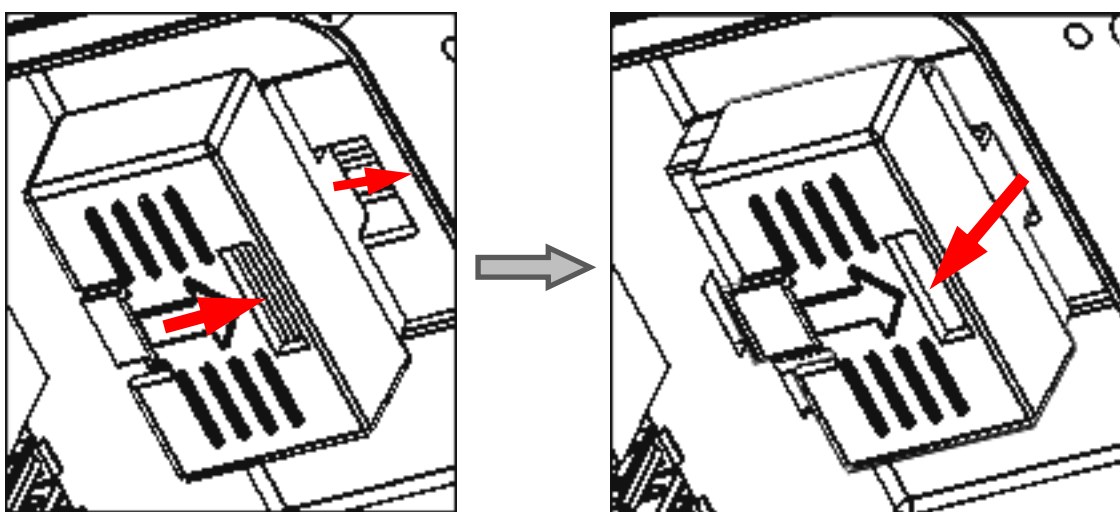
Извлечение крышки, фиксирующей ФН в корпусе
